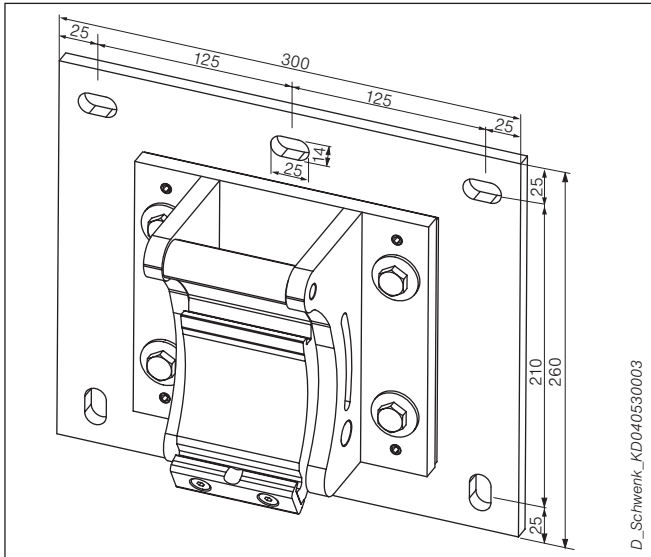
Consola tipo D – Fijación mural con placa de montaje ajustable
